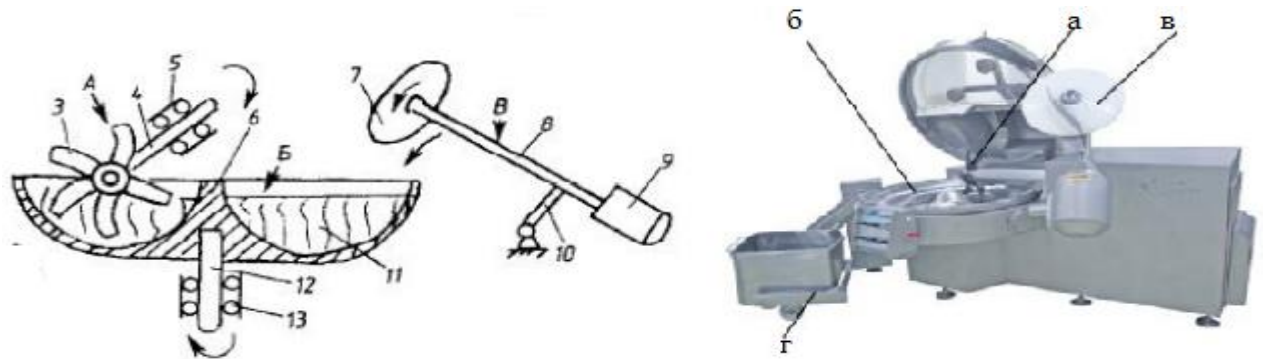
Схема чашкового кутера: 1 - візочок; 2 – підіймаючий пристрій; 3 - ножова головка; 4 - вал ножа; 5, 13 - опори підшипника; 6 - чашка; 7 - тарілочка; 8 – вал; 9 - двигун; 10 - штанга; 11 - сировина; 12 - вал; А – механізм різання; Б – подавальний механізм; В - вивантажування; Г - завантажування
